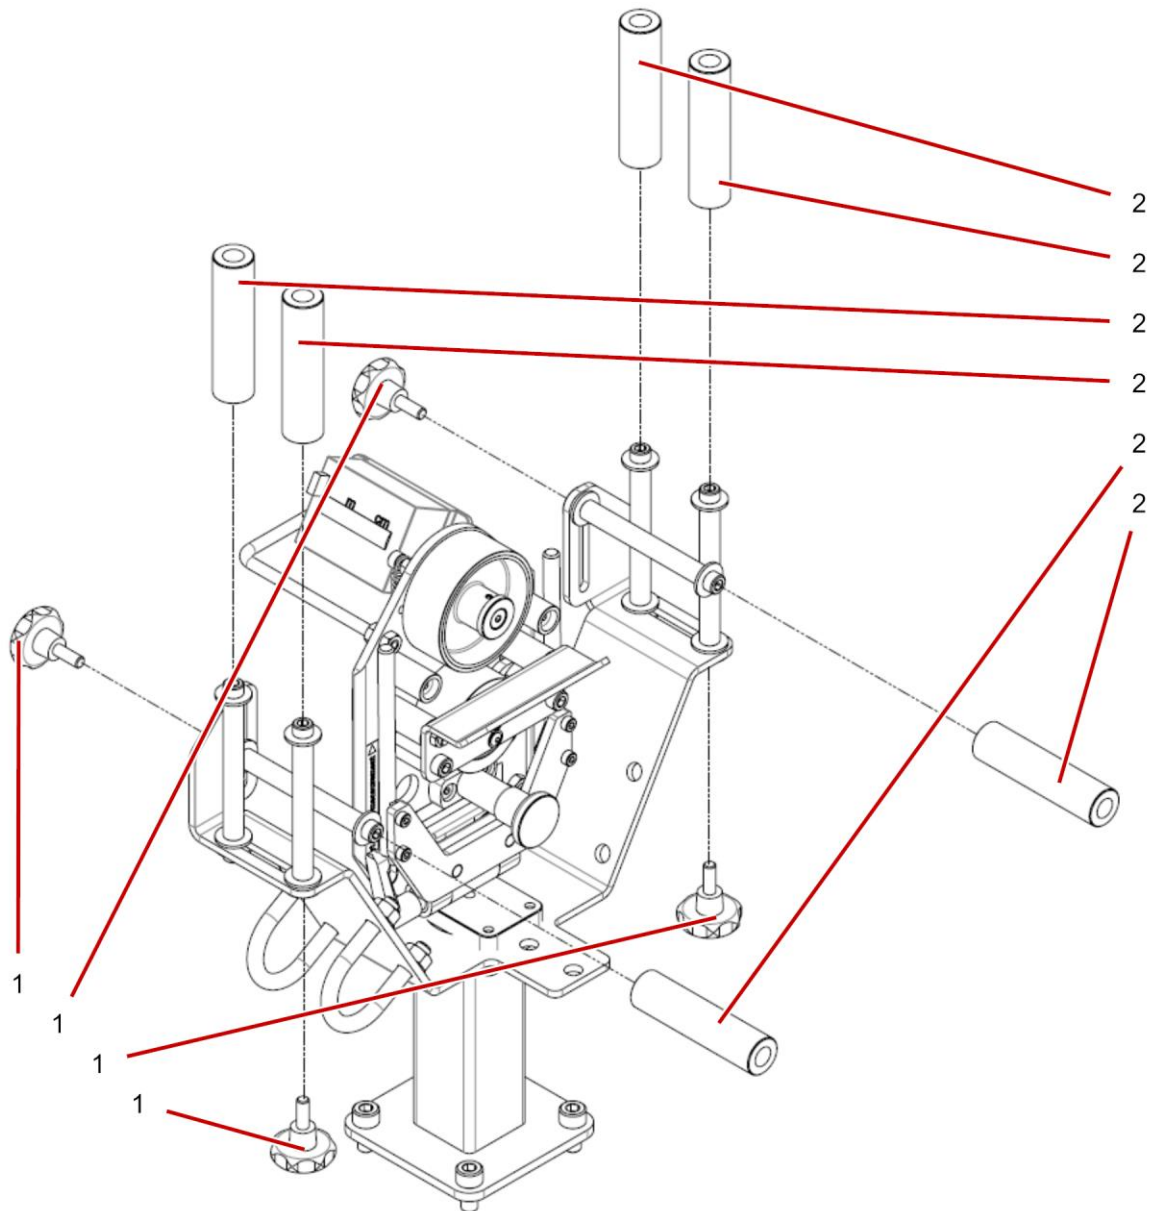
Pièces de rechange des cages de roue - MESSBOI 25
